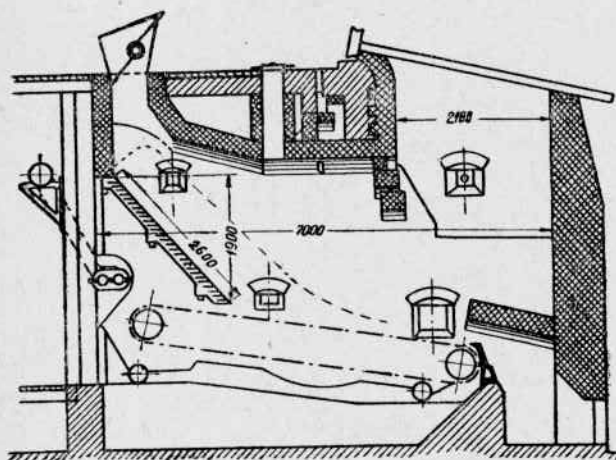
Ступенчатая топка с цепной решеткой для дробленки.
